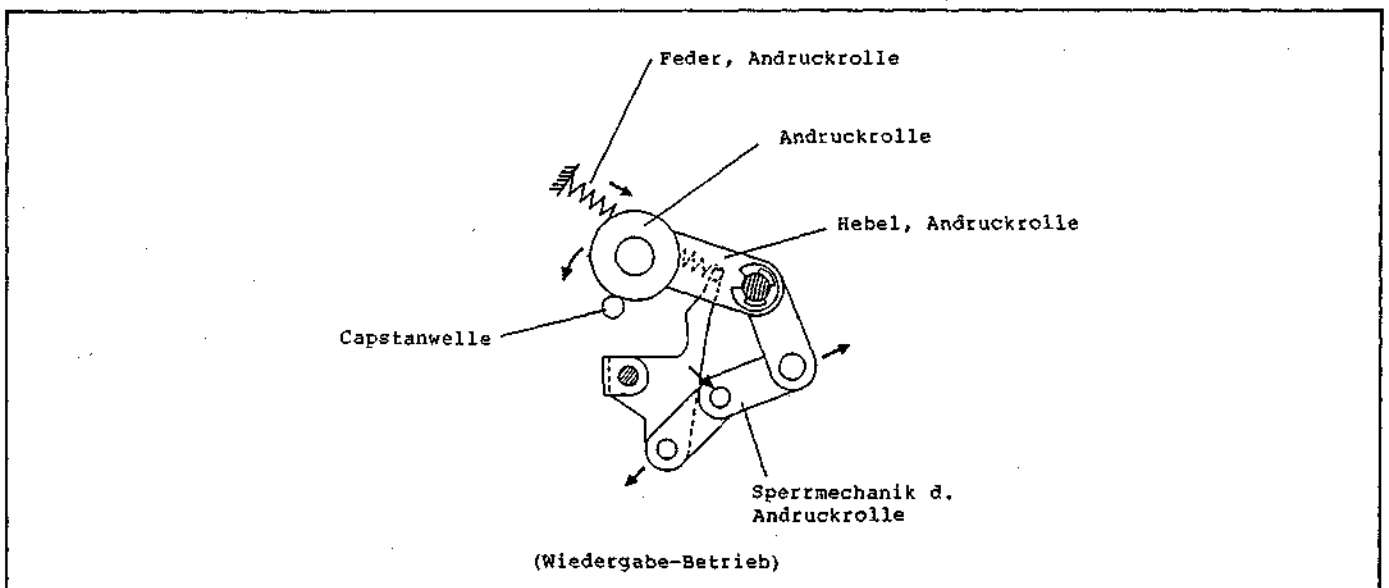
Steuermechanismus für die Andruckrolle (Abspielbetriebsart)
